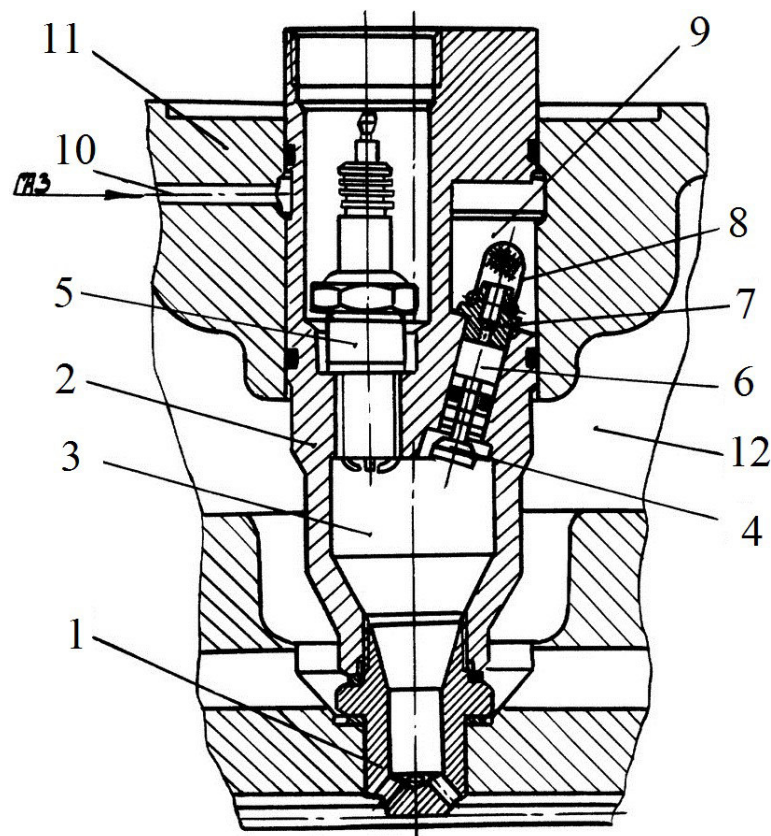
Форкамера: 1 – розпилювач; 2 – корпус; 3 – робоча порожнина;
